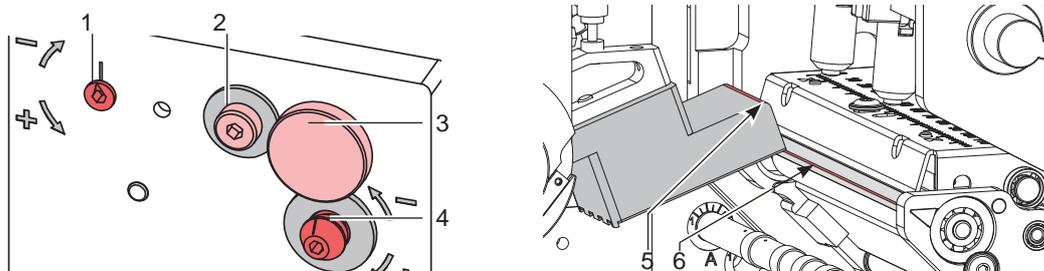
Ausrichten des Stempels zur Spende- oder Druckerkante
